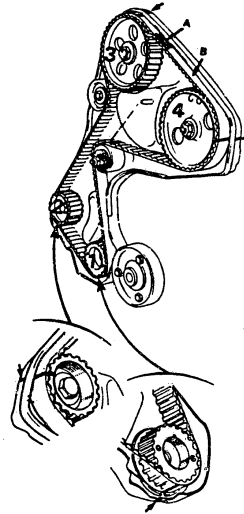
Das Einstellen der Motorsteuerung. Vor dem Auflegen des Zahnriemens sind die Zahnriemenräder korrekt auf die Markierungen auszurichten. Ferner ist die Laufrichtung des Riemens zu beachten. 1 Kurbelwellenrad – 2 Wasserpumpenantriebsrad – 3 Nockenwellenrad – 4 Einspritzpumpenantriebsrad.
